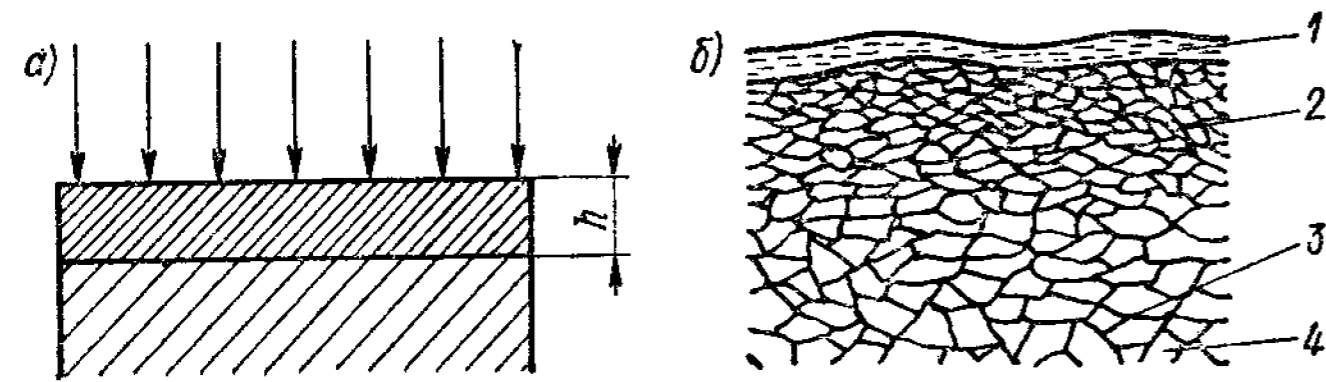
Поверхностный слой (а) и схема его строения после механической обработки (б)
